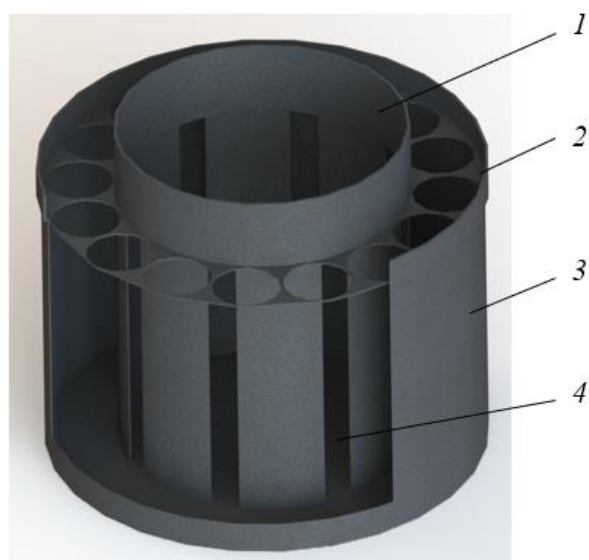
Трехмерная модель центробежного сепарационного устройства с соосно расположенными трубами (вид с разрезом): 1 – входной патрубок внутренней цилиндрической трубы, 2 – решетка с круглыми отверстиями, 3 – корпус сепарационного устройства, 4 – прямоугольные щели
